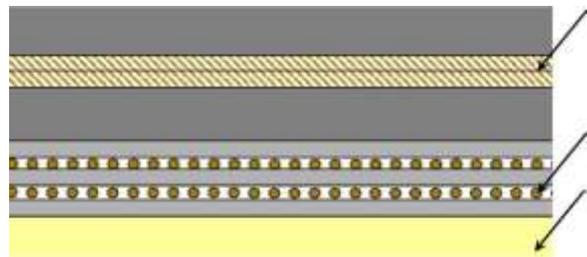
Разрез трехслойного гибкого резинотехнического трубопровода: 1 - верхний огнестойкий слой; 2 - слой с армирующей металлической сеткой; 3 - внутренний рабочий гидроизоляционный слой
